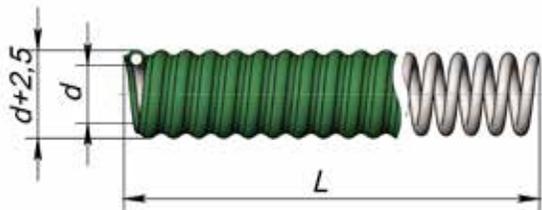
Конструкция и габаритные размеры трубки армированной
